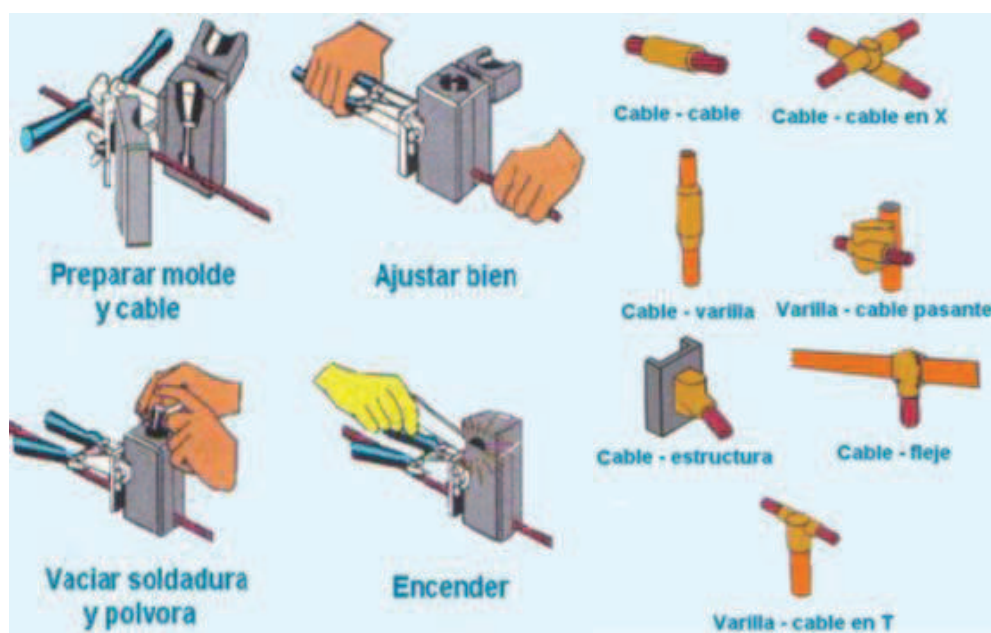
Proceso de aplicación de Soldadura Exotérmica.
